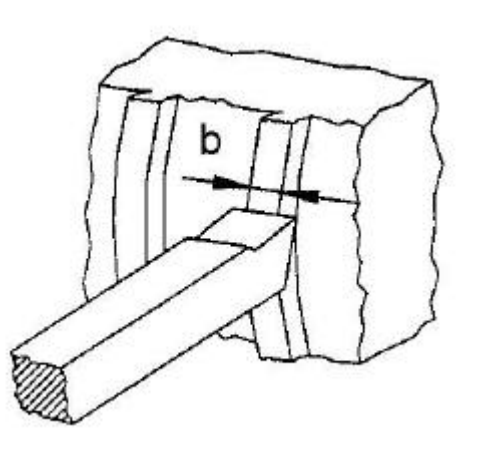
Exemplo de corte ortogonal (fonte: Machado e Silva).
